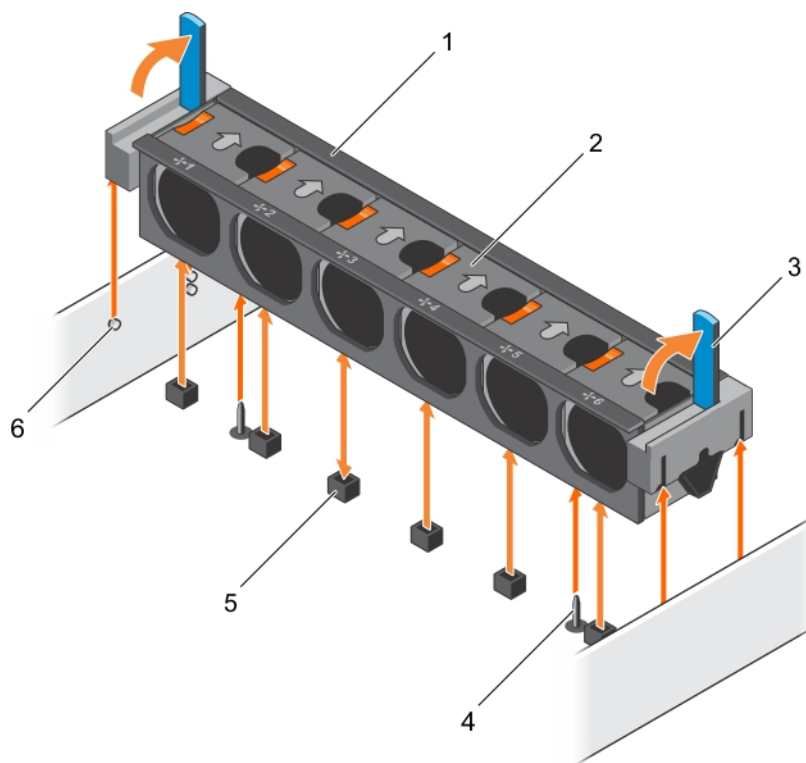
Entfernen und Installieren der Lüfterbaugruppe
